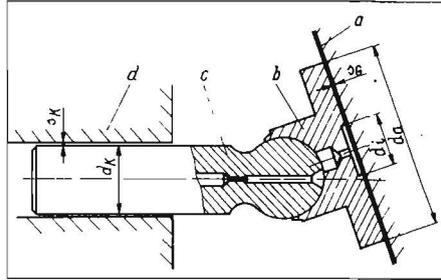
Gleitpaarungen Kolben—Zylinderbohrung und Gleitschuh—Schrägscheibe; a Schrägscheibe, b Gleitschuh, c Kolben, d Zylinder
